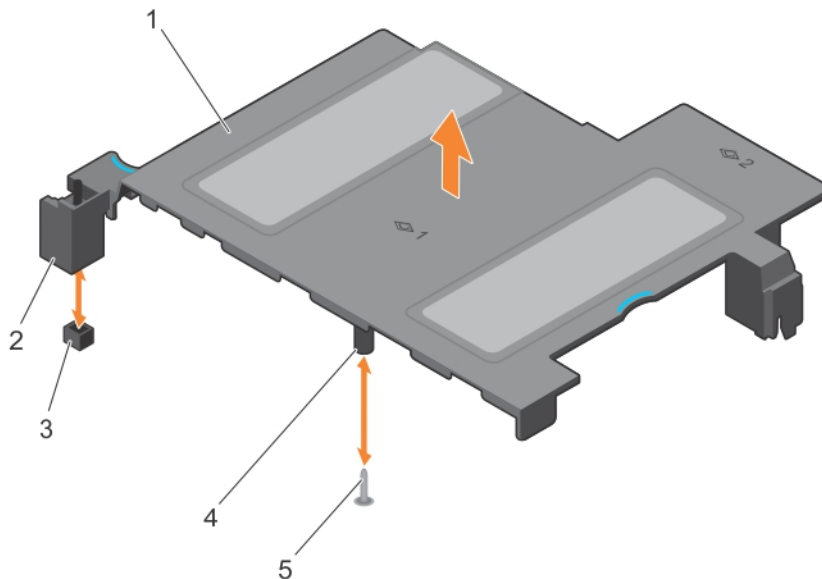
Extracción e instalación de la cubierta de refrigeración
